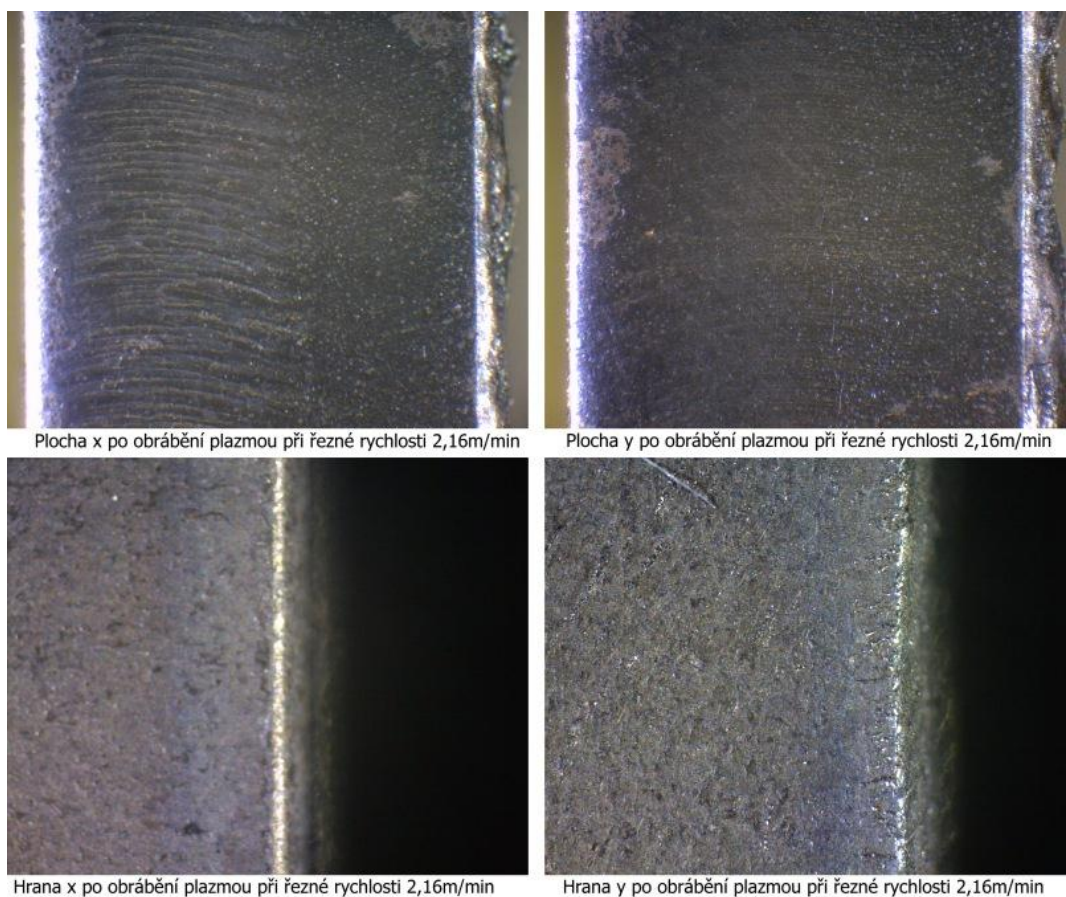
Snímky z mikroskopu vzorku 4 obráběného plazmou - materiál 11 375
